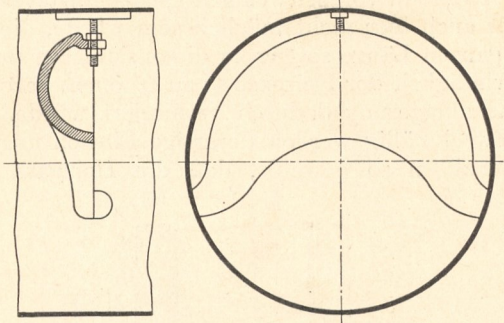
Flammrohreinsatz aus Gußeisen. Ausführung: Otto Thost, G. m. b. H., Zwickau.
